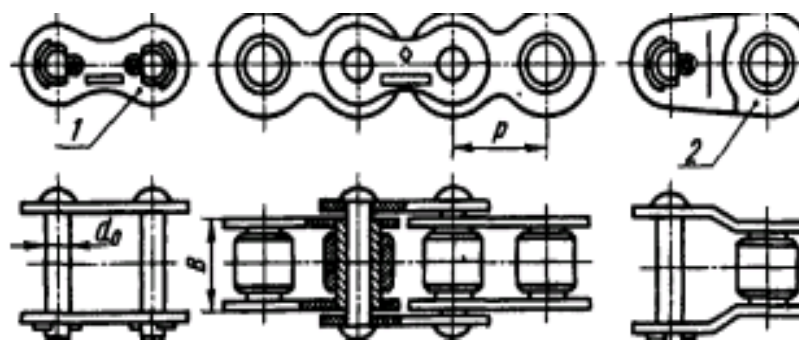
Приводний роликовий однорядний ланцюг:
